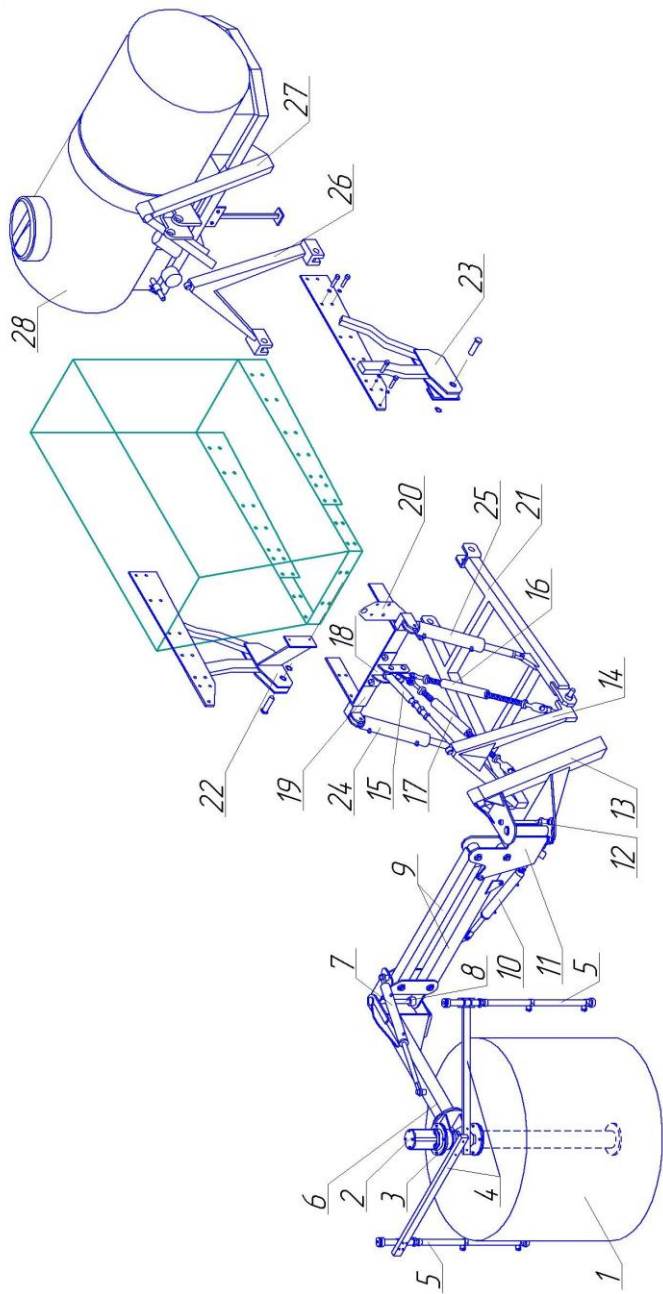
Устройство и схема сборки ЩБ0-25 ПЛ.
